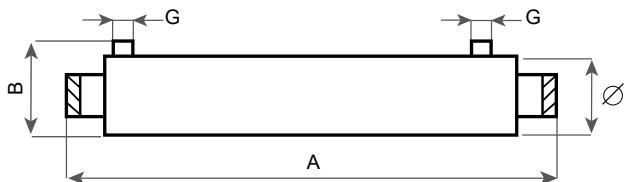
Внешний вид и габаритные размеры УФ-установок.
